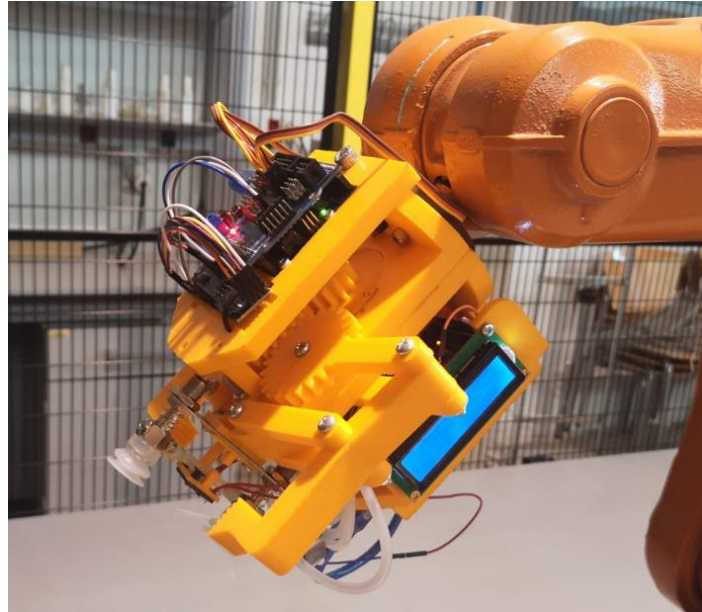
82. Ensamblaje herramienta completa (Vista derecha)
